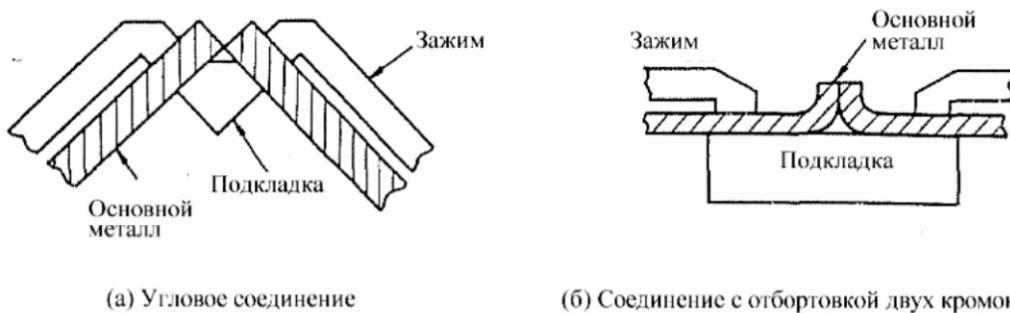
Приспособления-прокладки для разных сварных соединений
